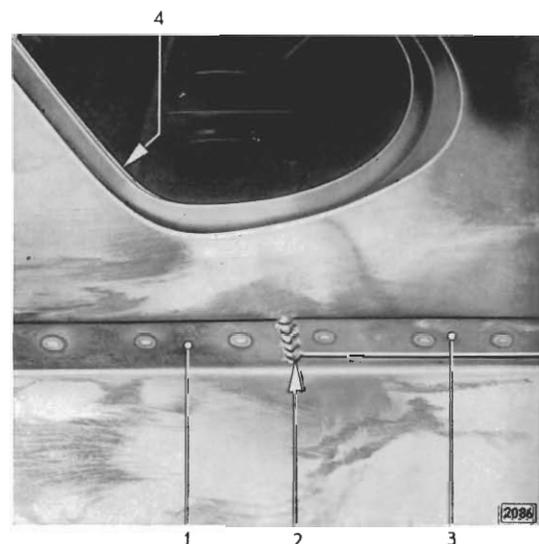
Einschnitt im oberen Seitenwandflansch unmittelbar hinter der Rückwandscheibensäule autogen zugeschweißt
